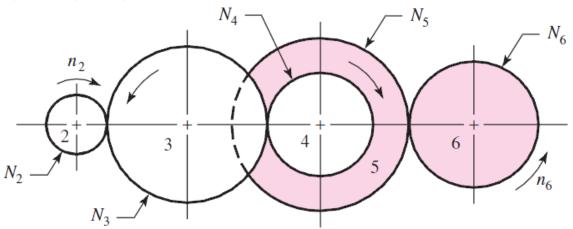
Trem de engrenagens (Shigley, Mechanical Engineering Design, 2011)
